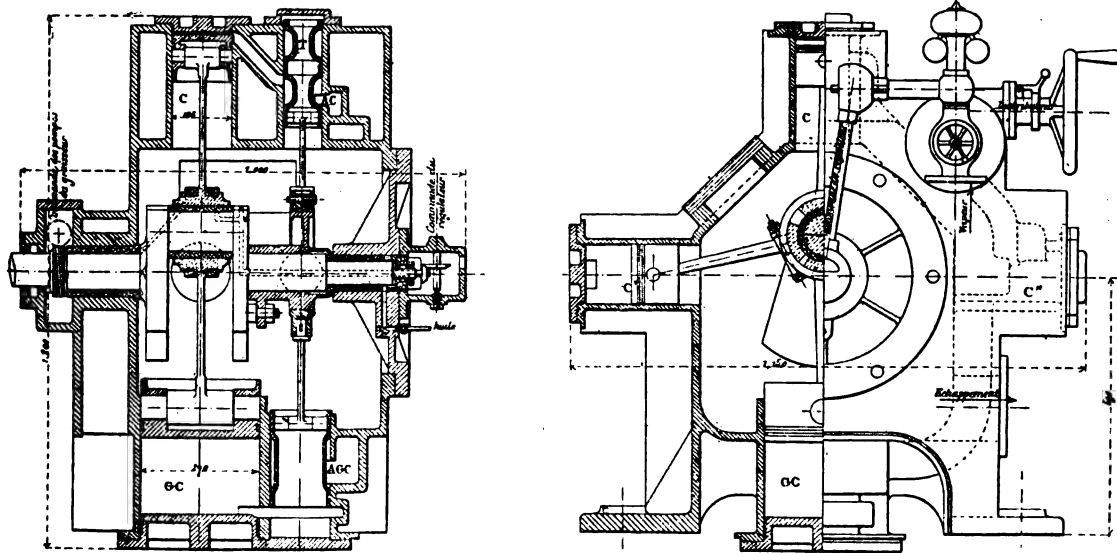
et 2. — Machine Lefèvre, type fixe.
